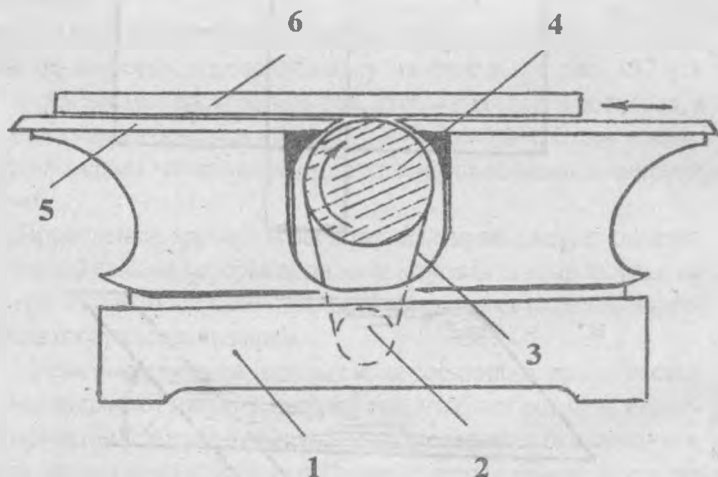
Барабанный шлифовальный станок: 1-станина; 2-электродвигатель; 3-ременная передача; 4-шлифовальный барабан; 5-стол; 6-заготовка
